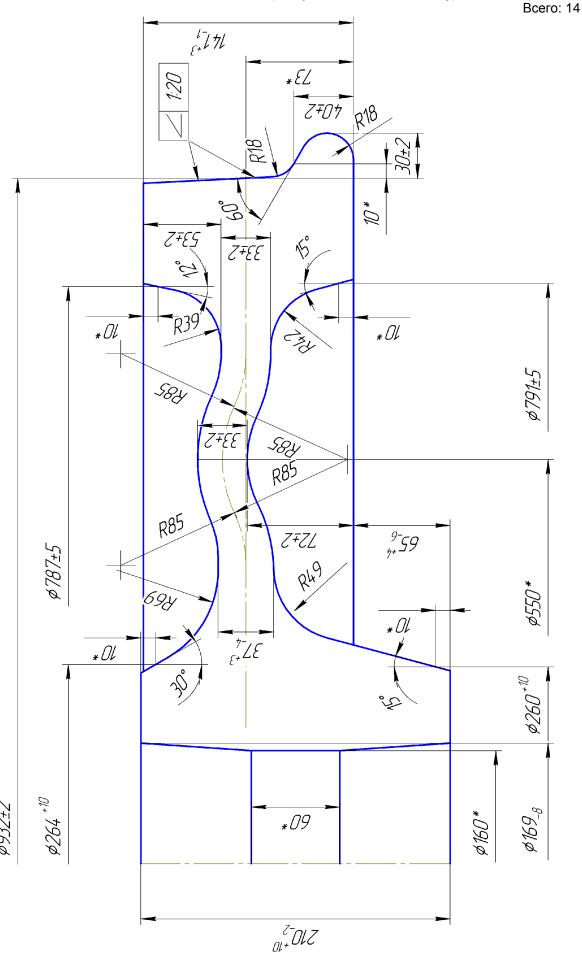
Колесо с черновой механической обработкой Ø 932 мм после участка І-й МО под колесо Ø 920 мм, чертеж № В.03.02.02.01. Масса колеса с обработкой к/к на 2/3 поля допуска = 459 кг.
